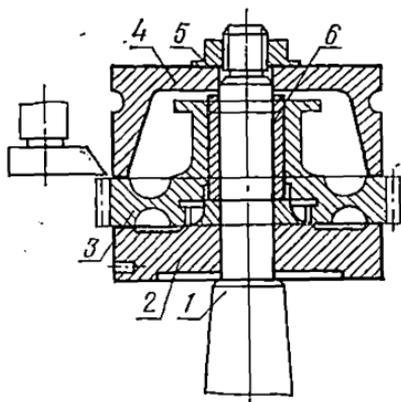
Приспособление с ручным зажимом для закрепления заготовки на зубодолбежном станке:
